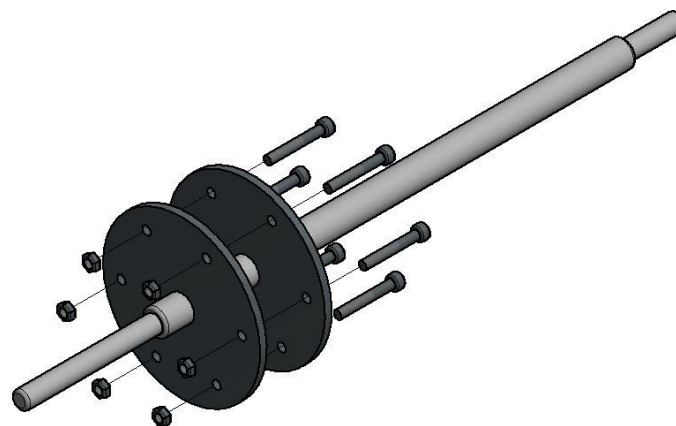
Ensamble de las bridas planas con el eje de la cámara de tostado.
